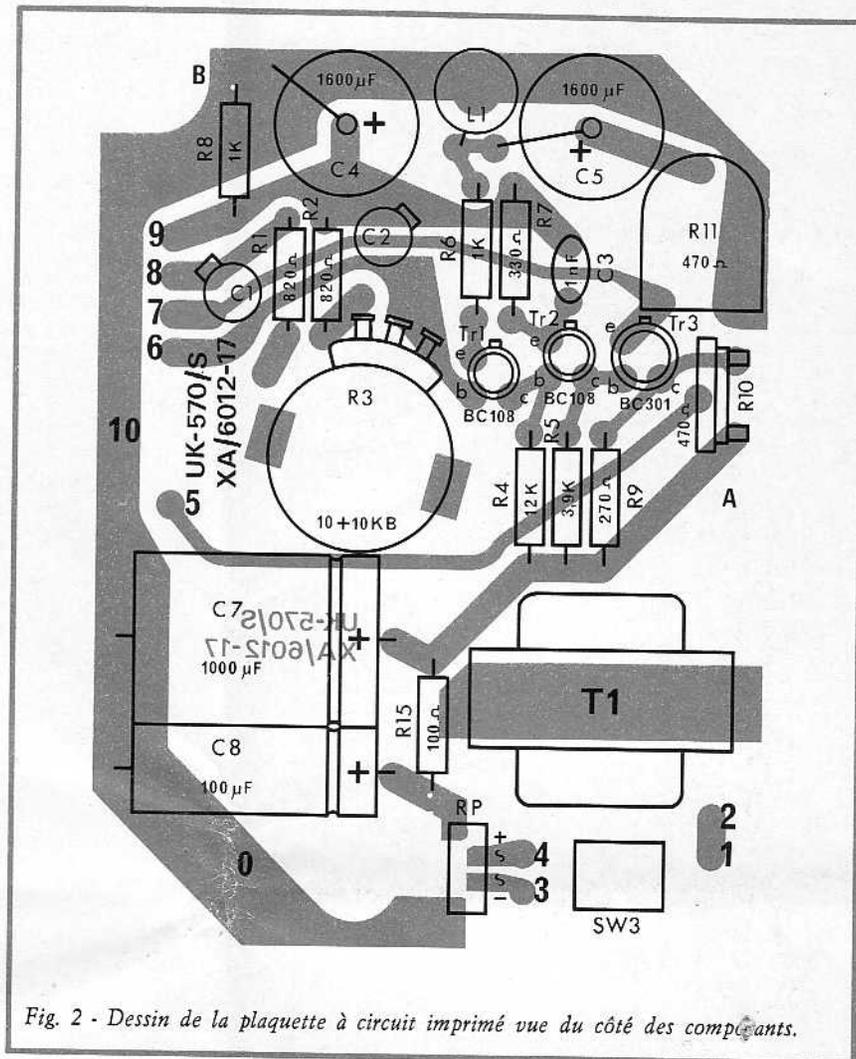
Dessin de la plaquette à circuit imprimé vue du côté des composants.
